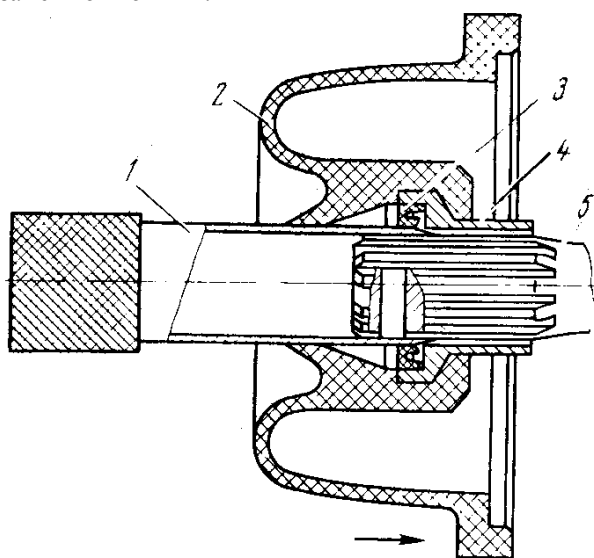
Приспособление, предохраняющее повреждение манжеты полуоси: 1 — оправка; 2 — защитный чехол; 3 — манжета; 4 — корпус манжеты; 5 — полуось.
